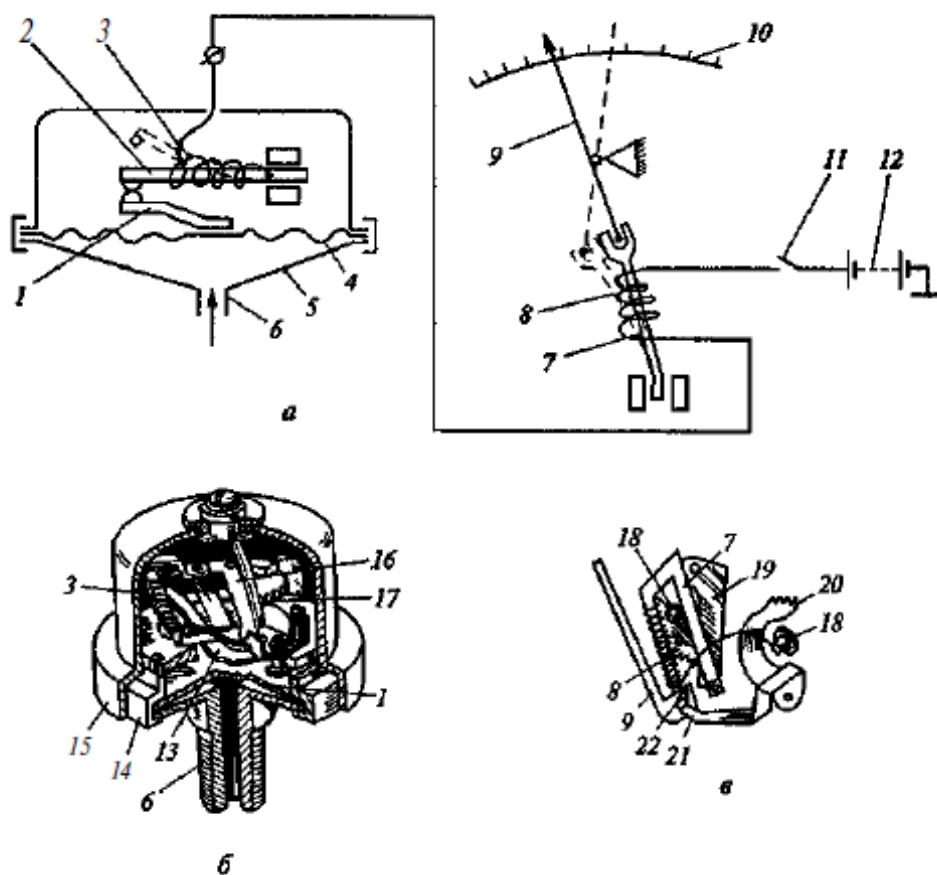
Принцип действия (а) и конструкция импульсного термобиметаллического датчика давления (б) и указателя (в) манометра: 1 – упругая пластина; 2 и 7 – биметаллические пластины; 3 и 8 – обмотки нагревателей; 4 – мембрана; 5 – корпус; 6 – штуцер; 9 – стрелка указателя; 10 – шкала; 11 – выключатель зажигания; 12 – аккумуляторная батарея; 13 – монтажное основание; 14 – крышка; 15 – контактная пластина; 16 – держатель; 17 – регулировочное устройство; 18 – вывод; 19 и 20 – зубчатые секторы регулировочного устройства указателя; 21 – пластинчатая пружина; 22 – крюк
